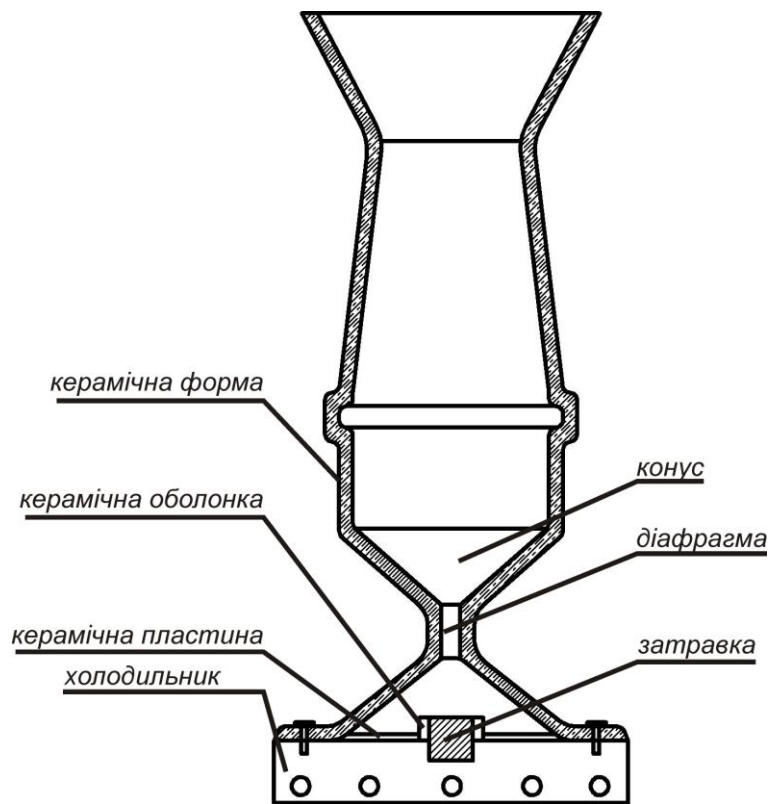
Схема ливарної форми для отримання монокристалічного виливка від затравки
